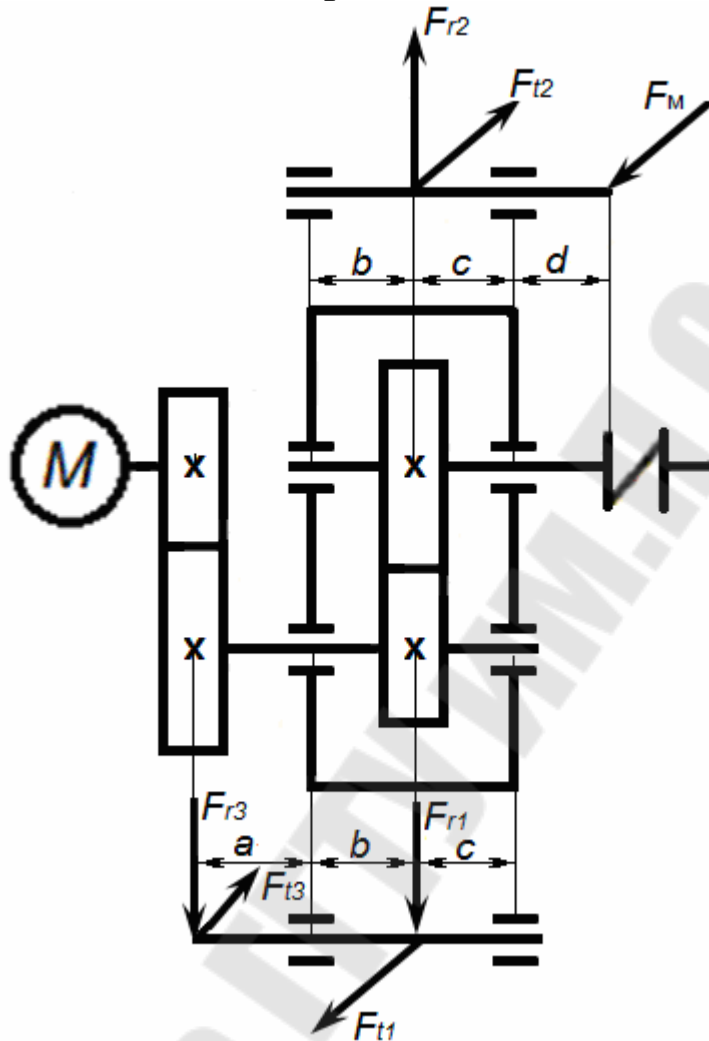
Привод конвейера с открытой цилиндрической зубчатой передачей
